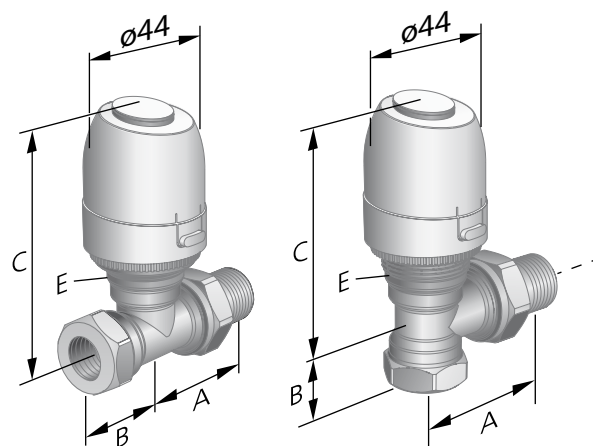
Клапан VALVE-S и VALVE-A с монтированным приводом ACTUATOR
